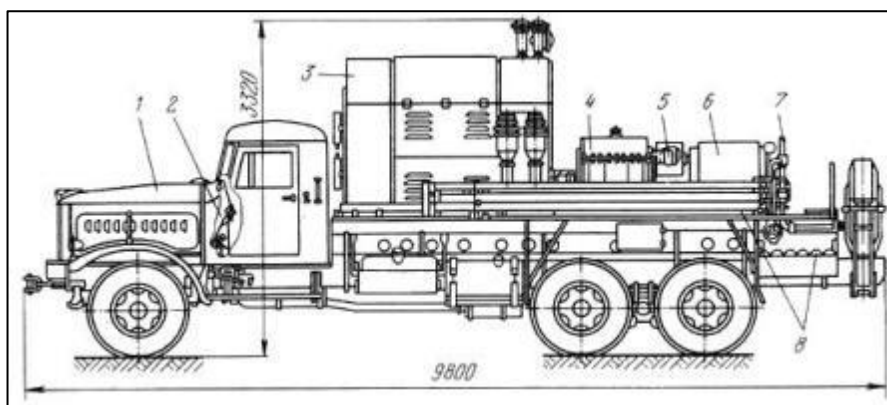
Насосный агрегат для ГРП 4АН-700: 1 - автомобиль КраЗ-257; 2 - кабина управления; 3 - силовой агрегат; 4 - коробка скоростей; 5 - муфта сцепления; 6 - насосный агрегат; 7 - выкидной маинфольд; 8 - соединительные трубы высокого давления
